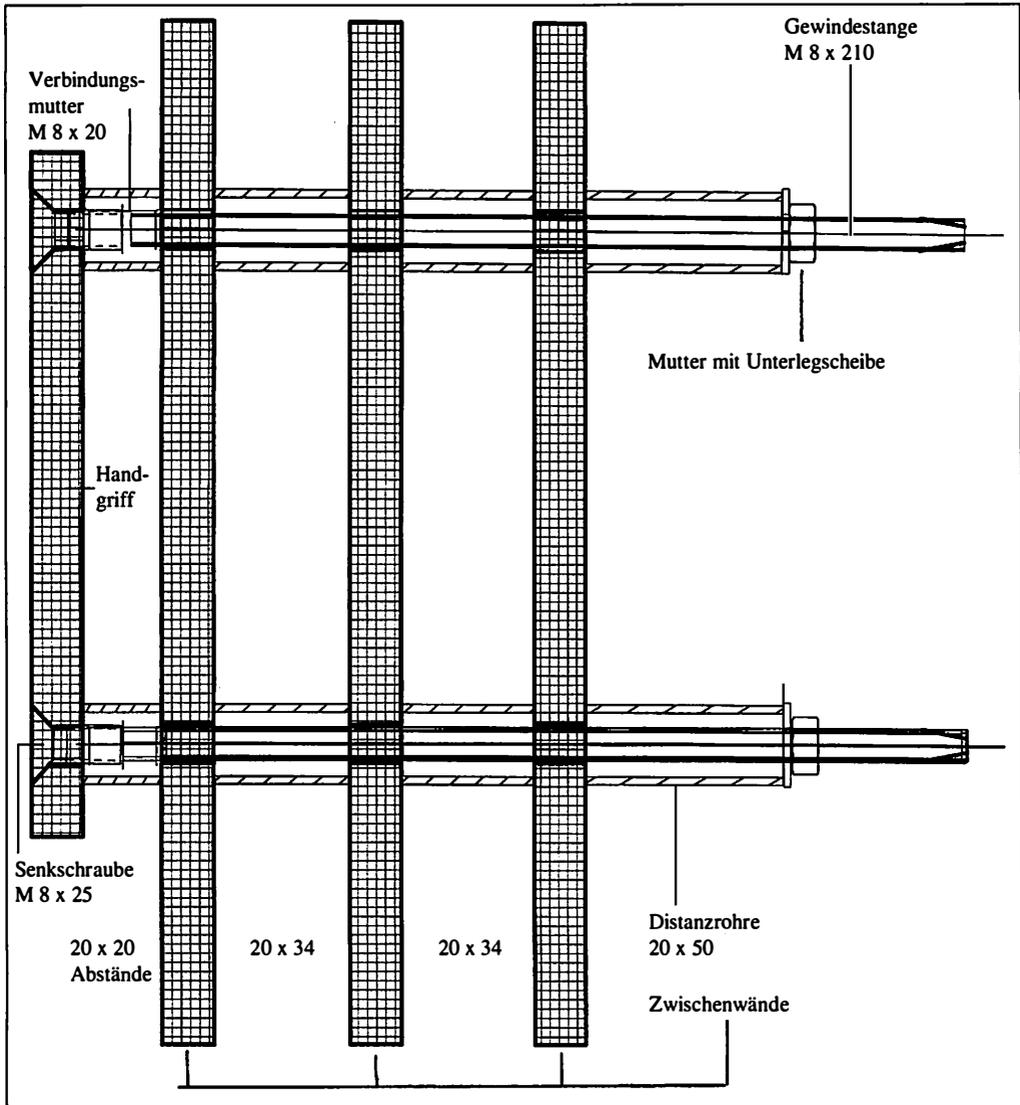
Skizze für den umgebauten und herausnehmbaren Einsatz in die Fledermaus-Großraumhöhle 1FW der Fa. Schwegler. Zeichnung: CHR. KUTHE
